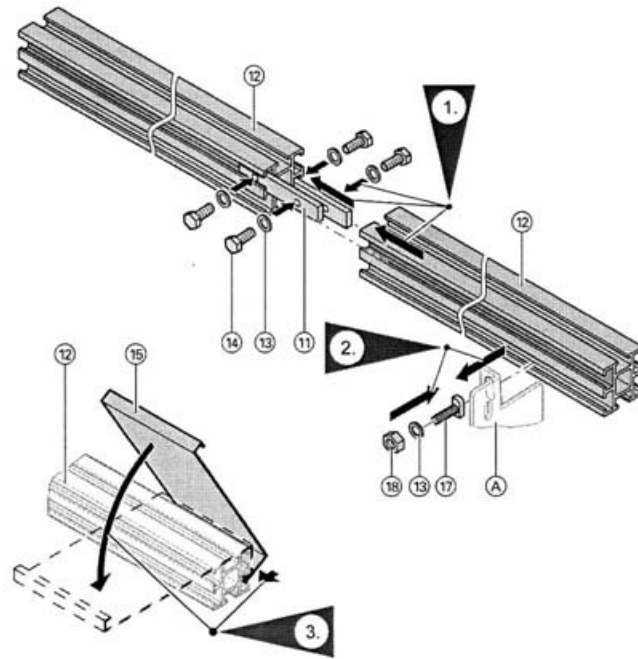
Montage des rails supports des capteurs sur les pattes de fixation à la toiture
